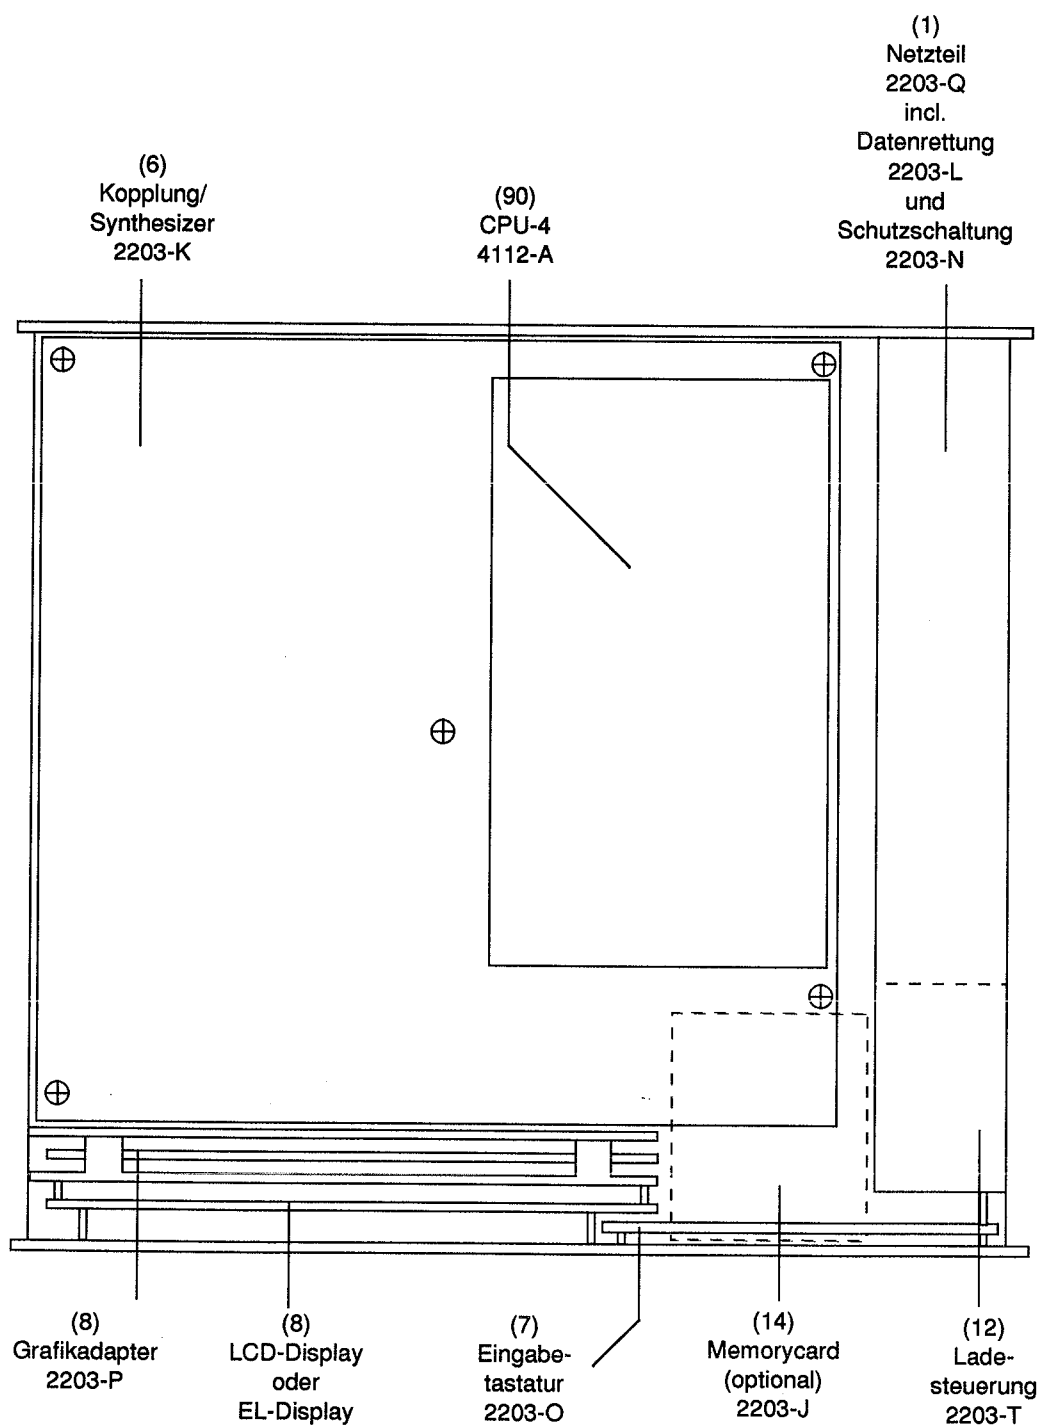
Lage der Baugruppen, Ansicht von oben
